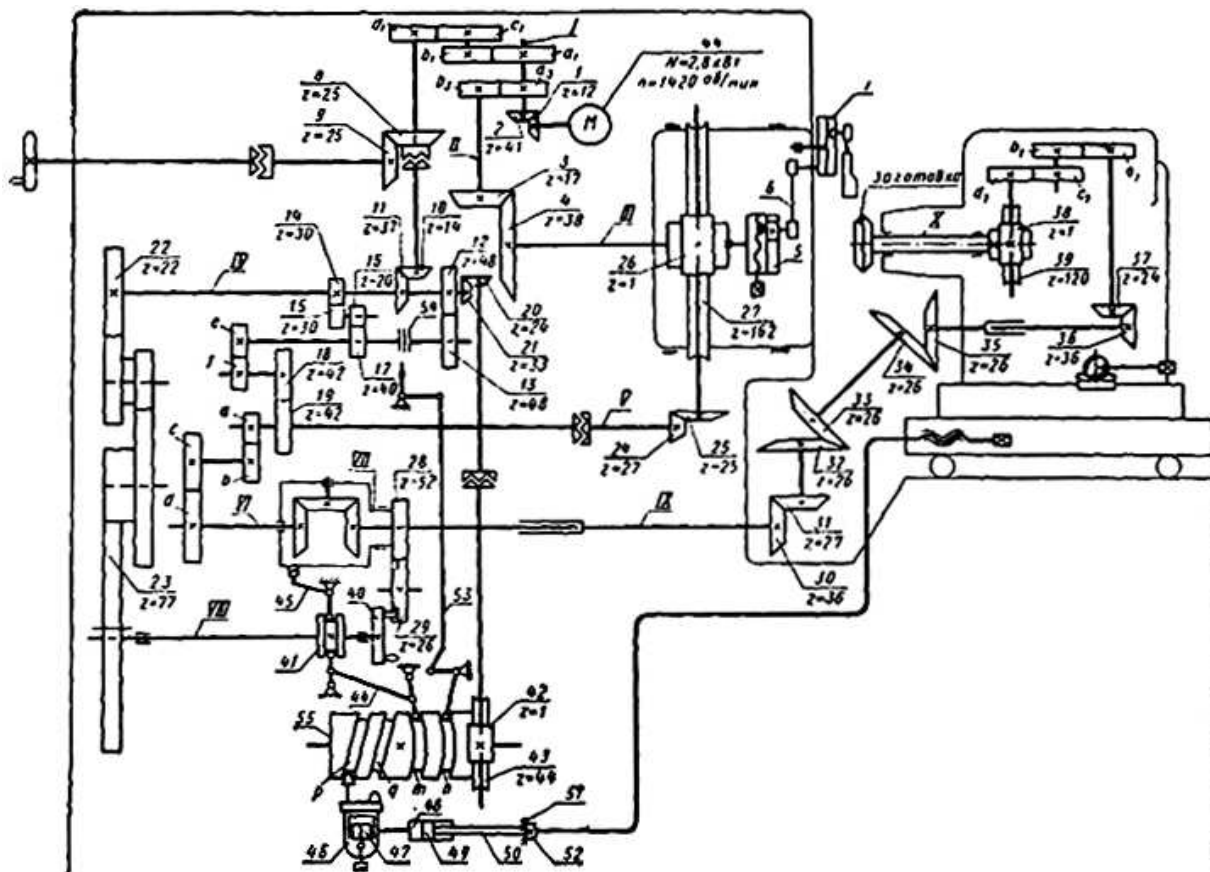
Кинематическая схема зубострогального станка для обработки прямозубых конических колес
